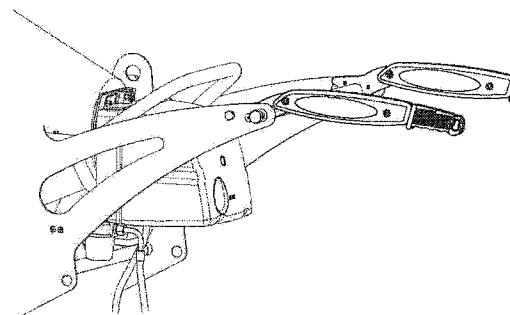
Ручки в положении транспортировки, нагреватель XL9.
